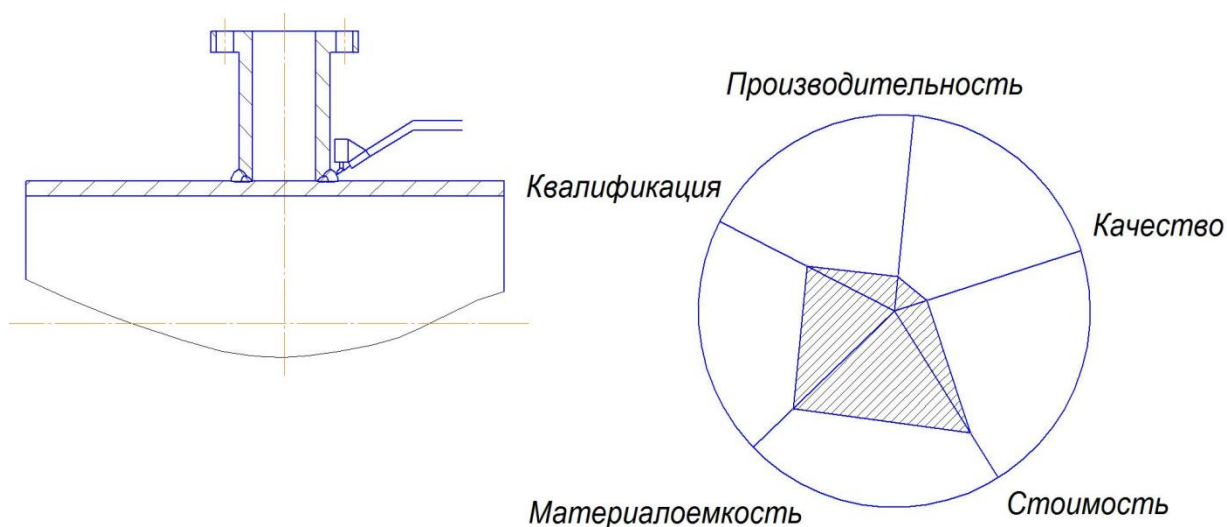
Механизированная сварка разветвленной дугой
